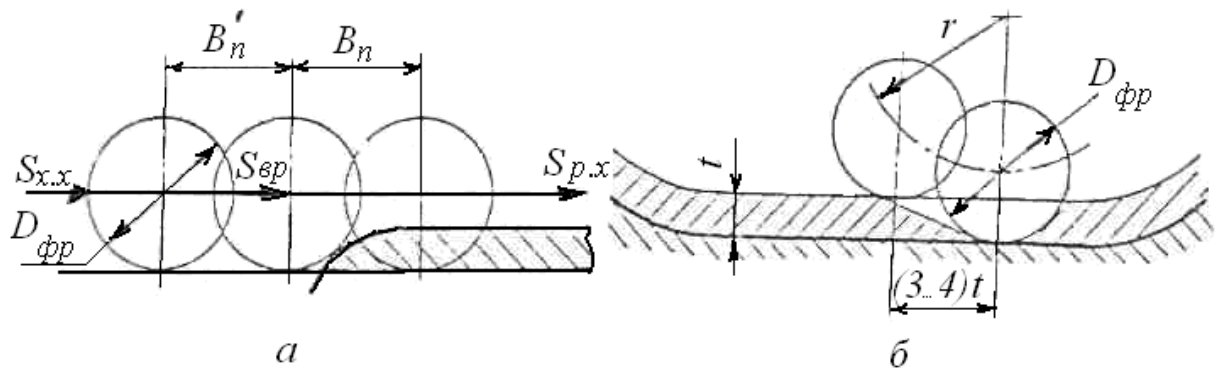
Схемы фрезерования для наружного контура (*а*); внутреннего контура (*б*)
